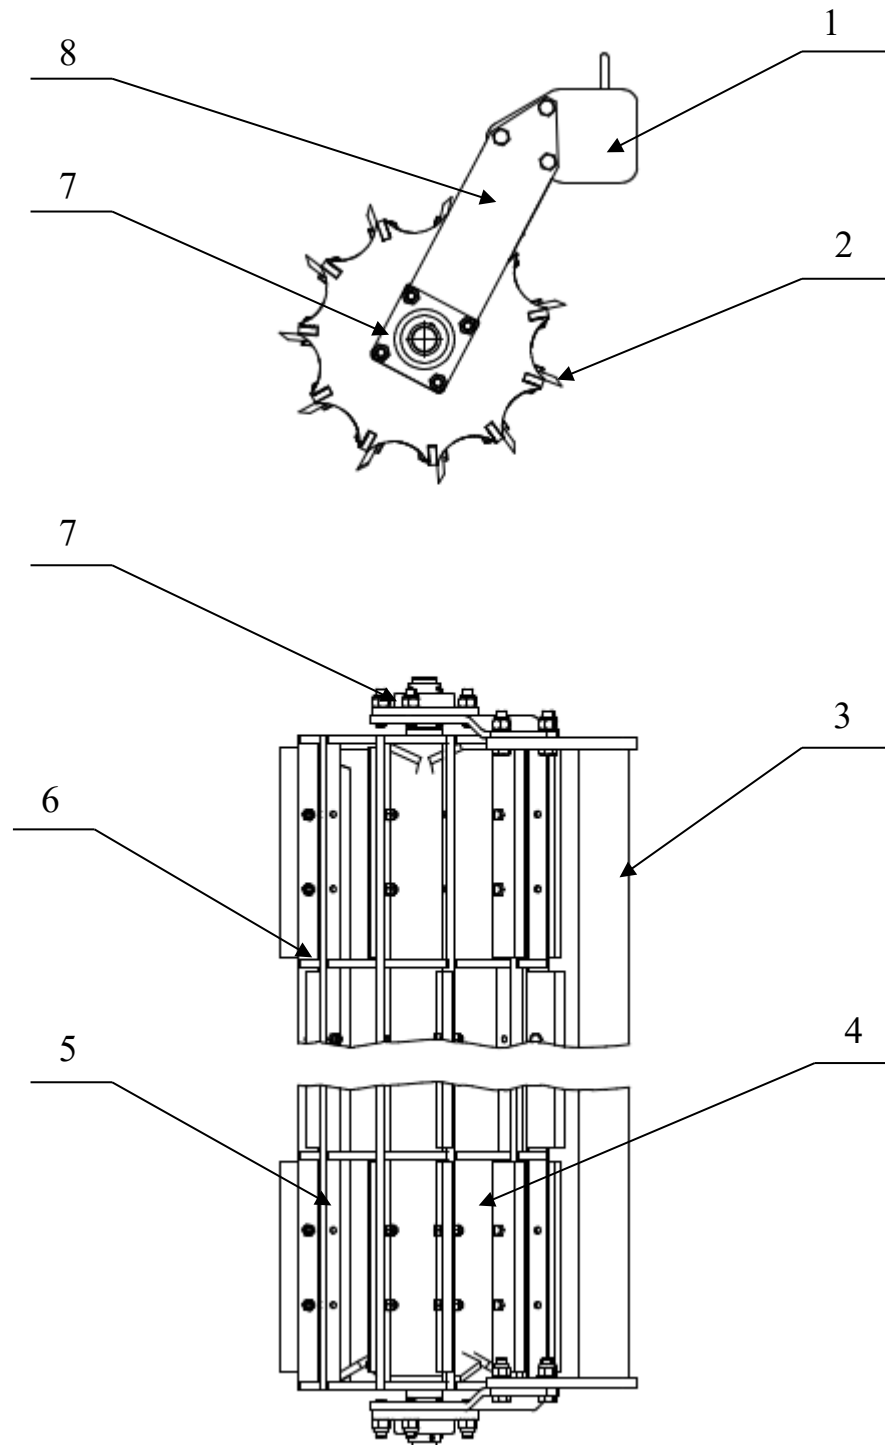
Загальний вид розробленої конструкції катка-подрібнювача:
